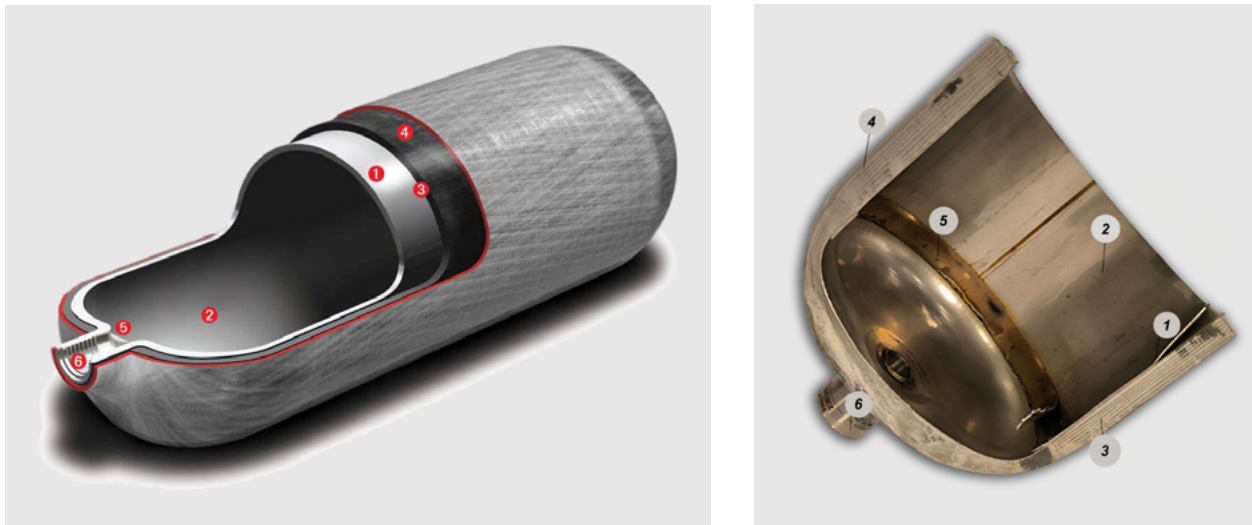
Пример металлокомпозитного баллона с лайнером из нержавеющей стали (слева – схематично; справа – фото в разрезе): 1 – лайнер из нержавеющей стали; 2 – внутренняя поверхность баллона; 3 – силовая оболочка из стекло- или углеволокна; 4 – защитный слой; 5 – сварной шов; 6 – горловина баллона с резьбой
